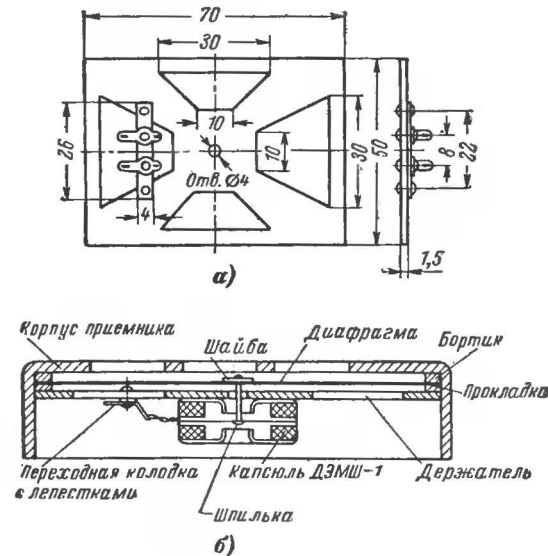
Громкоговоритель плоской конструкции, выполненный на базе капсюля ДЭШМ-1, и его расположение в корпусе приемника.
